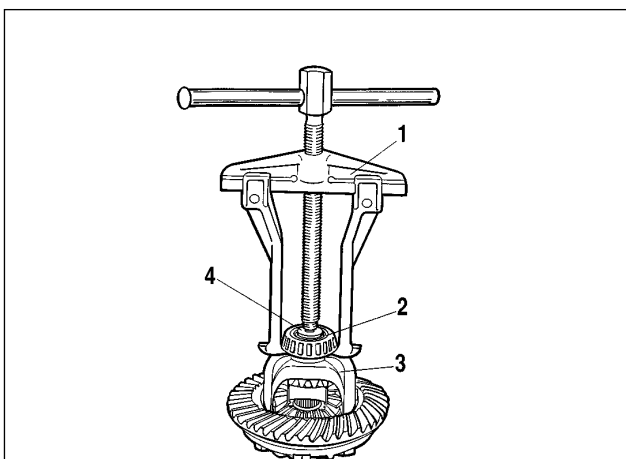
Ausbau des Innenrings des hinteren Lagers von Differentialgehäuse mit Universal-Abziehvorrchtung A.40005/1/6:
